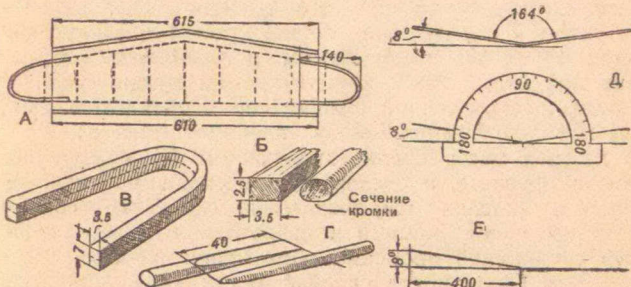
Изготовление крыла: А — чертеж крыла и размеры кромок, Б — сечение кромок, В — закругление (обод) и его размеры, Г — способ соединения кромки и закругления, Д и Е — способ построения поперечного V крыла.
